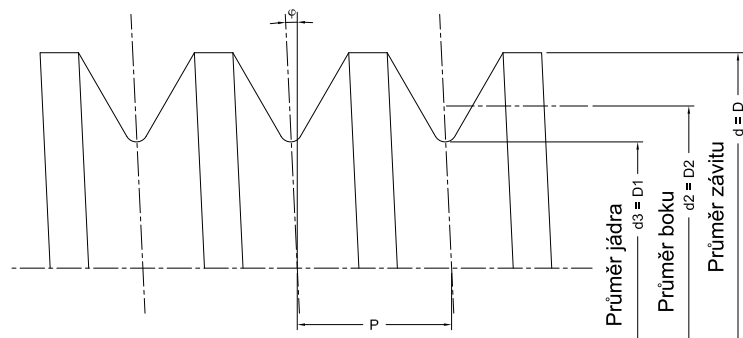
Pravý závit se šroubem otáčejícím se doprava
